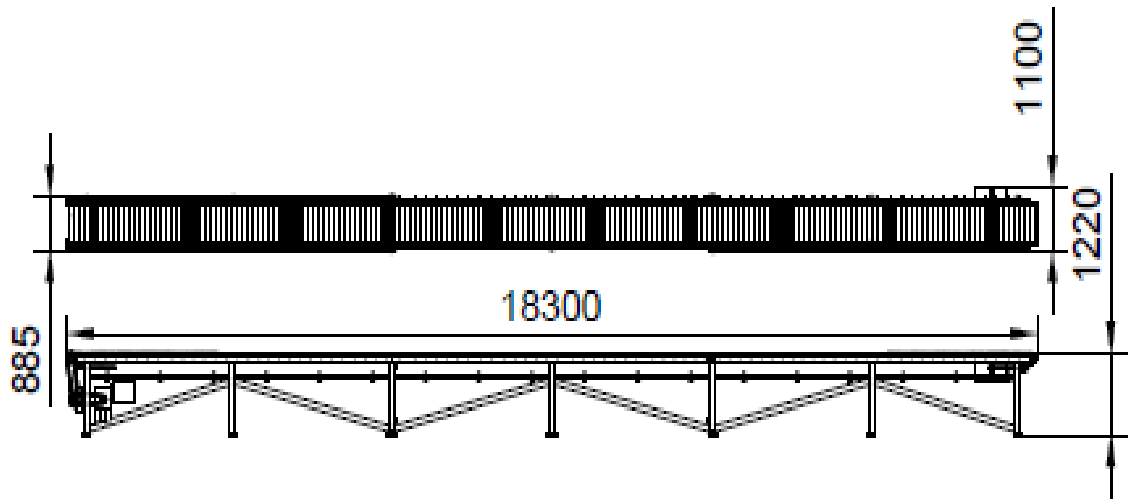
Габаритные размеры. Пластинчатый конвейер.
